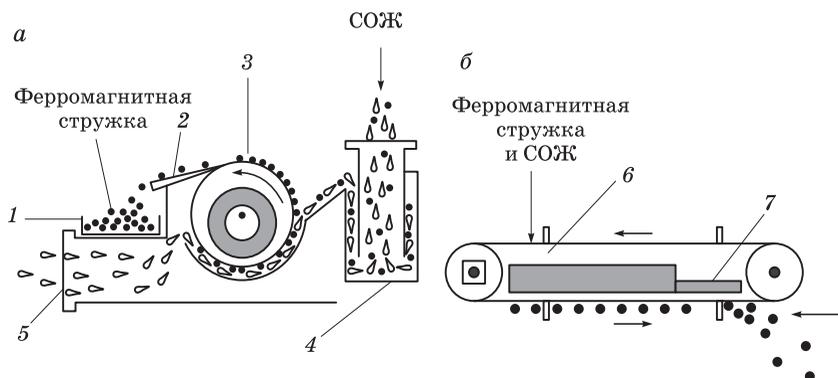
Схемы работы магнитного сепаратора (а) и магнитного конвейера (б):
